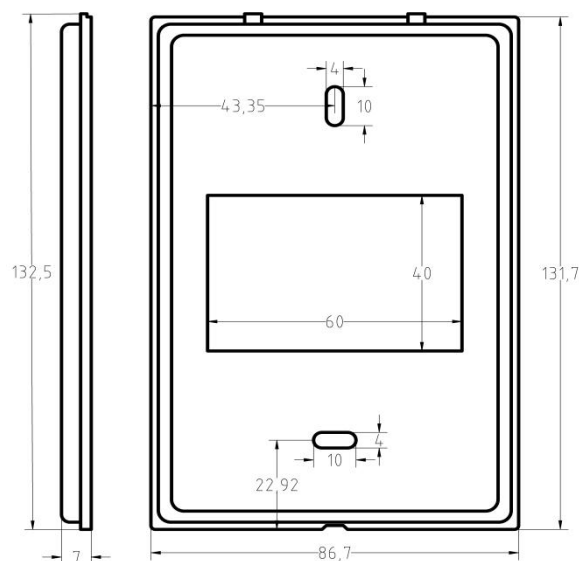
Dimensões da tampa traseira do produto, em milímetros (mm).
